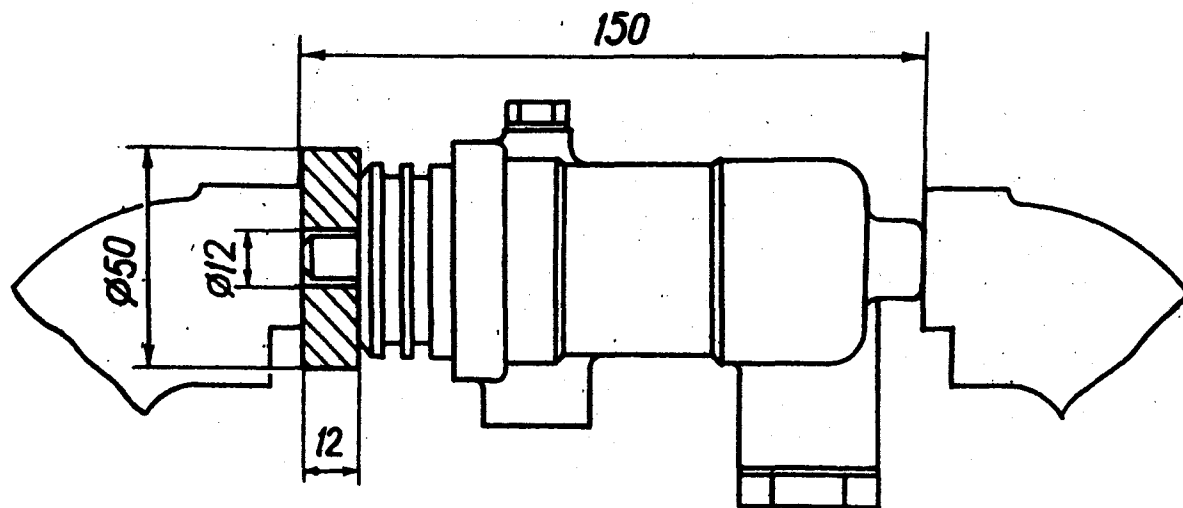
Разборка вторичного корпуса главного тормозного цилиндра
